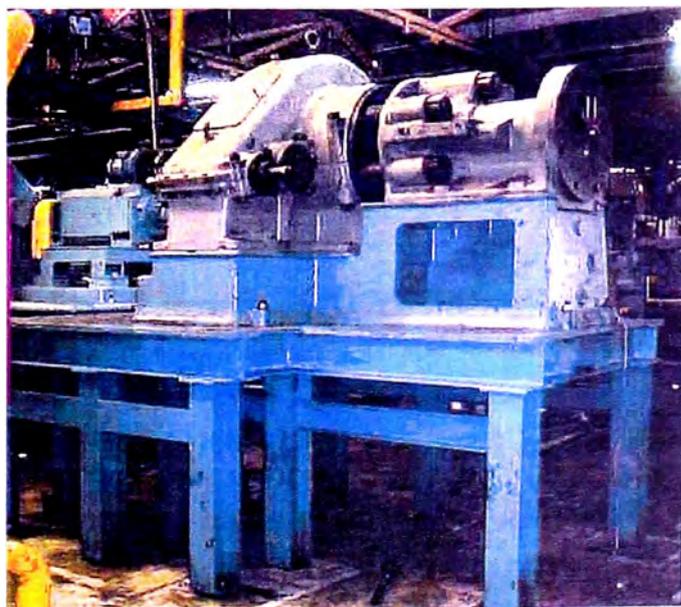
BASE ACERO FIJA LADO CAPA
